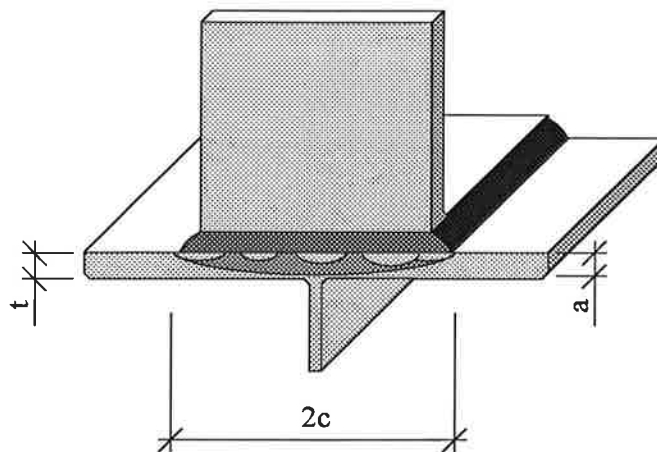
Section fissurée avant et après l'unification des fissures.
